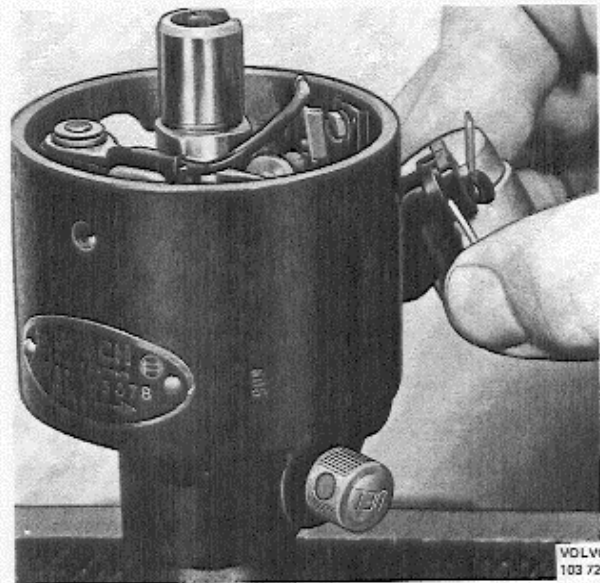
Ausbau der Primäranschlußklemme, B 20 B
